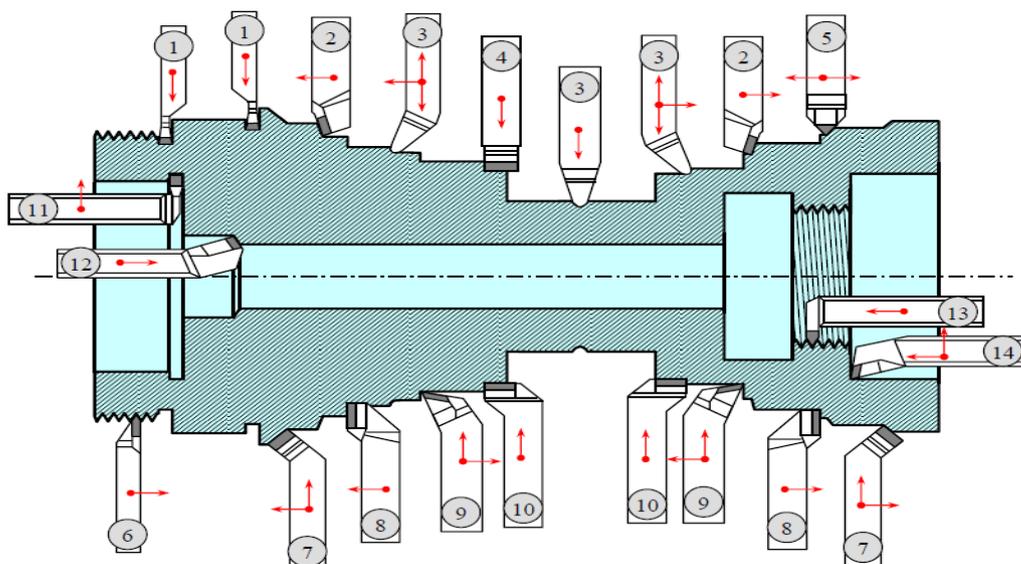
Outils de coupe du procédé de tournage. [6]
